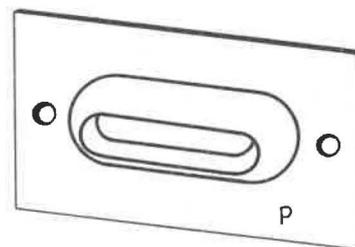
Porte clavetée sur la face trapézoïdale du moule M.
